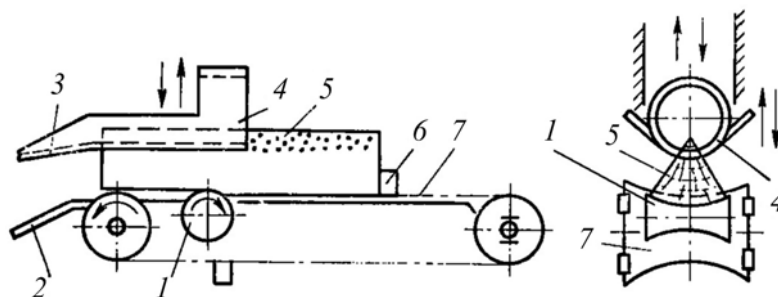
Кинематическая схема балансово-вырабатывающего станка Н-10
